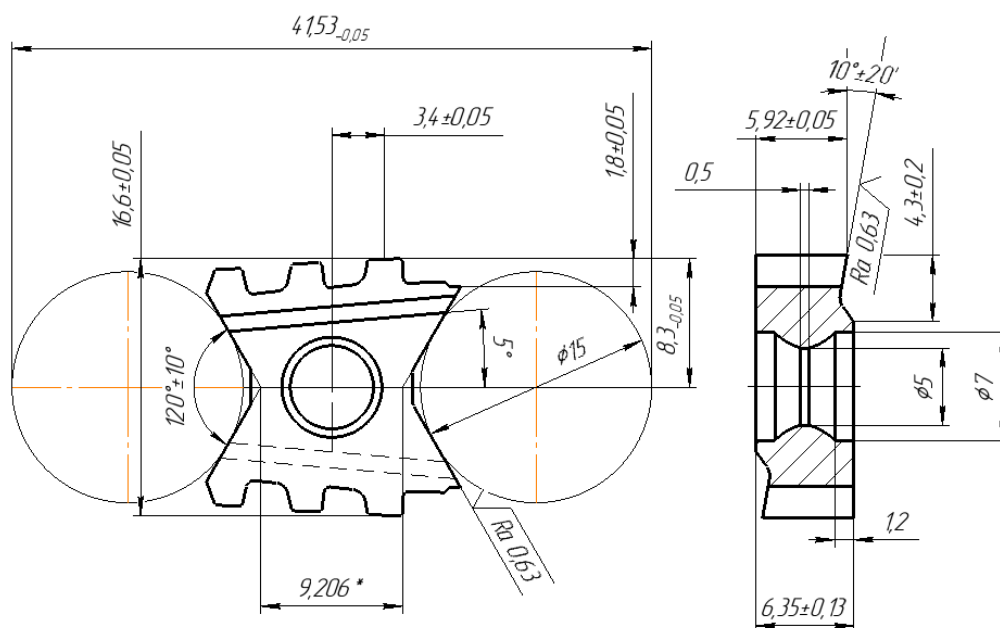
Конструкция сменной твердосплавной двусторонней режущей пластины типа "гребенка" для нарезания трапецеидальной (упорной) конической резьбы
